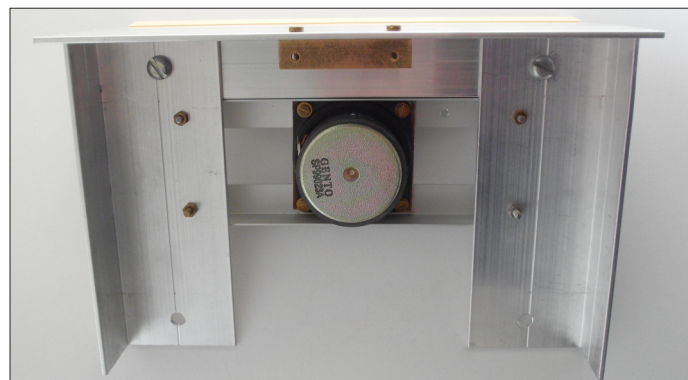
Wegen der Anschlüsse in Printmontage bleiben die Seiten des Junior 1D offen.
